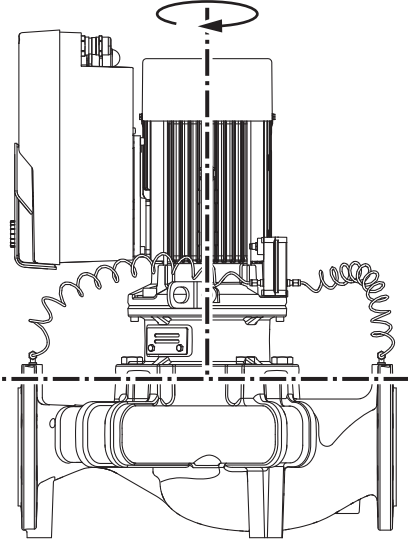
Dikey motor mili ile izin verilen montaj konumları
